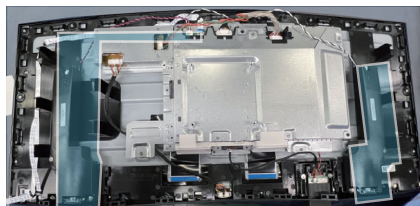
Collegamento del cavo altoparlante e installazione delle viti
